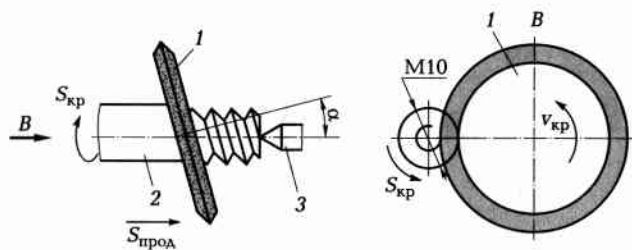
Схема шлифования резьбы односточным абразивным кругом
